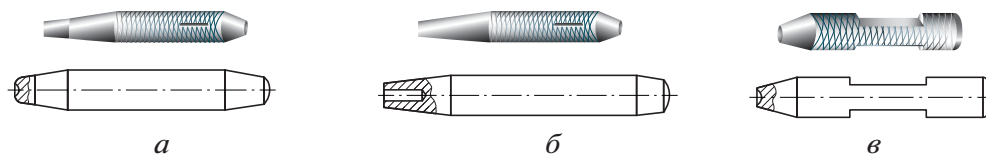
Вспомогательный инструмент для клёпки: *а* — обжимки; *б* — натяжки; *в* — поддержка
